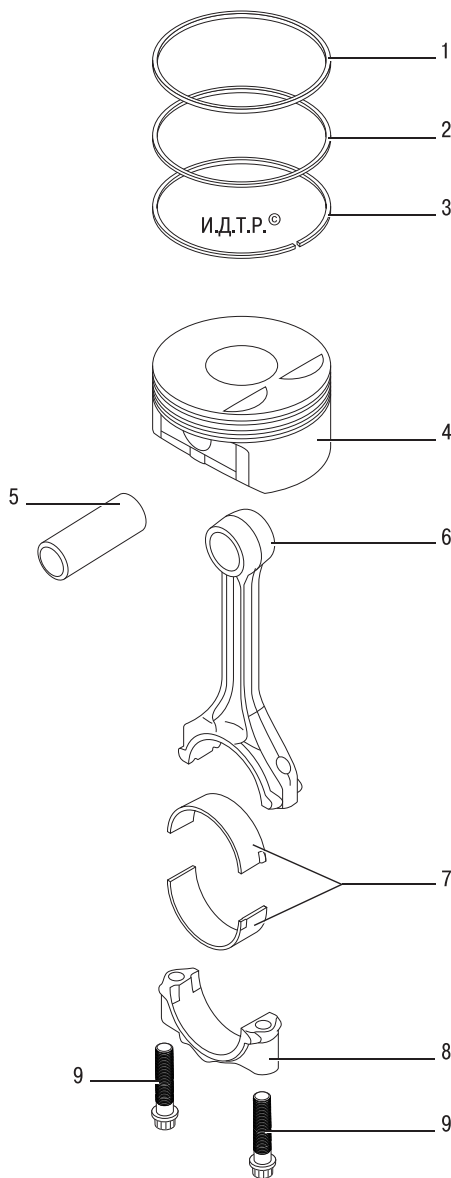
Детали шатунно-поршневой группы: 1 – верхнее компрессионное кольцо; 2 – нижнее компрессионное кольцо; 3 – маслосъемное кольцо; 4 – поршень; 5 – поршневый палец; 6 – шатун; 7 – шатунные вкладыши; 8 – крышка шатуна; 9 – болты крепления крышки шатуна
